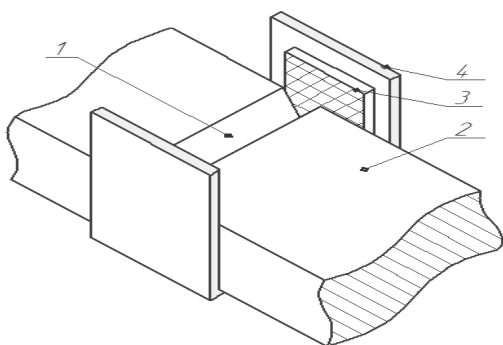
Схема сварки короткого стыкового соединения
